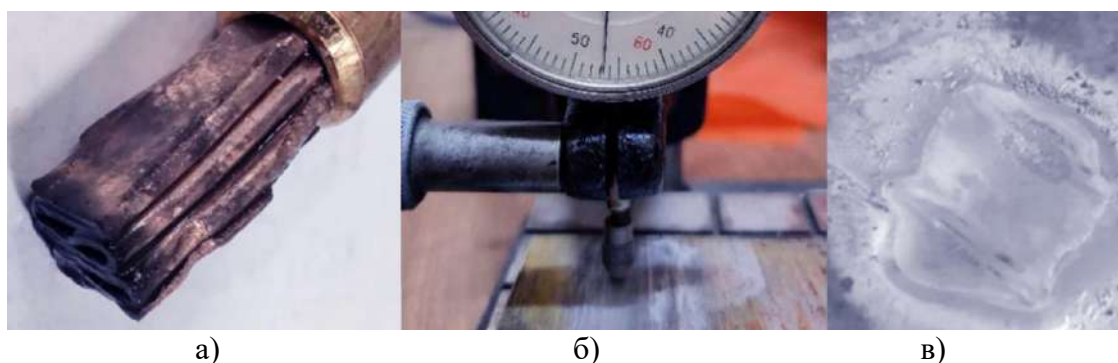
Внешний вид электрода-инструмента и поверхности после электролитно - плазменной обработки: а) электрод инструмент типа гармошка; б) образец из стали 08X18H9T ($Gv = 28$ л/ч); в) образец из стали 20X13 после пиления, удаление с поверхности 470 мкм за три прохода ($Gv = 28$ л/ч, $S=278$ мм/мин)
